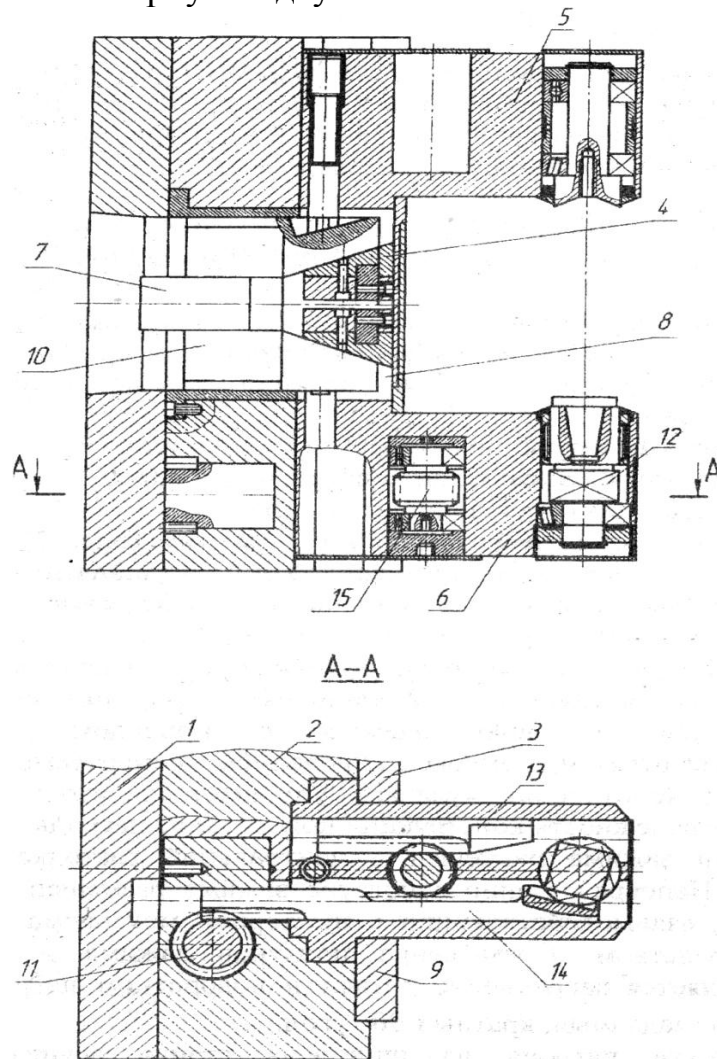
Конструкция поворотного патрона с клиновым устройством зажима
